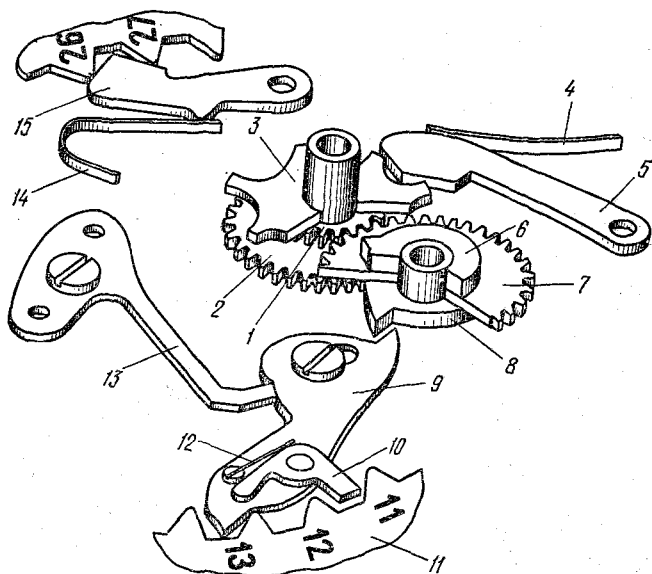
Кинематическая схема двойного календаря часов «Слава»: 1 — первое колесо календаря, 2 — часовое колесо, 3 — звездочка, 4 — пружина, 5 — фиксатор звездочки, 6 — палец, 7 — суточное колесо, 8 — кулачок, 9 — переключатель, 10 — собачка, 11 — кольцо календаря, 12 — пружинка собачки, 13 — пружинка переключателя, 14 — пружина фиксатора, 15 — фиксатор
